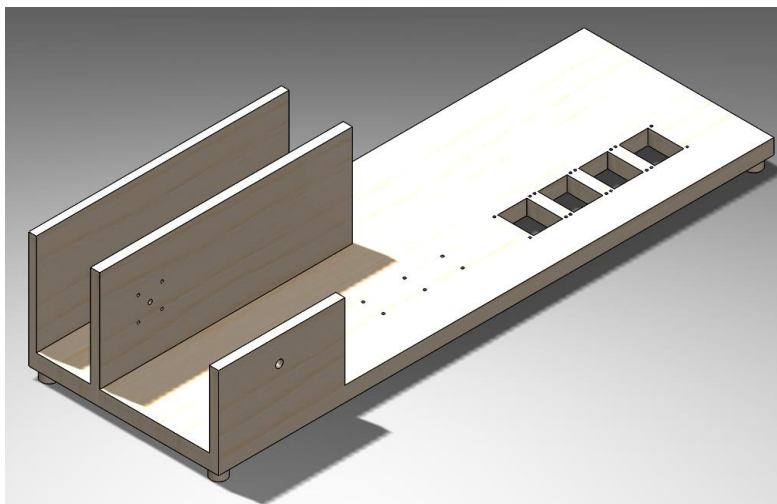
Base montada com furos sinalizados para haste e fixação do motor.
